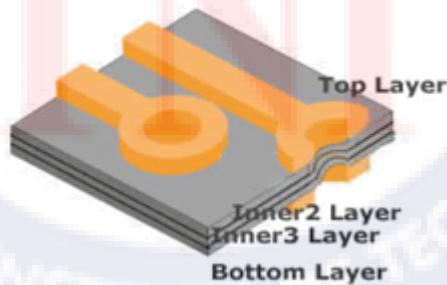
แสดงแผ่นวงจร พีซีบี (PCB) ชนิดสองหน้า (Double Side Plate through Hole)
